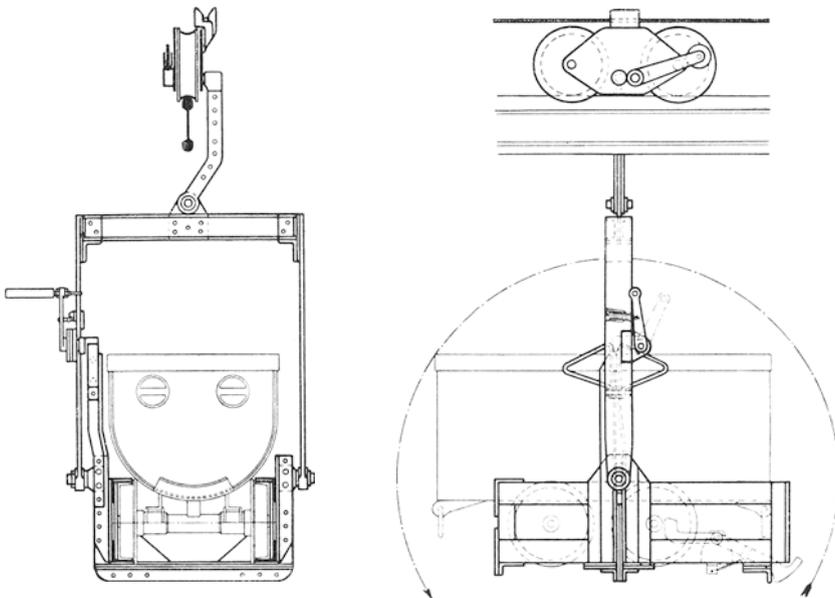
Grubenwagen auf kippbarer Plattform (Kaiser).
